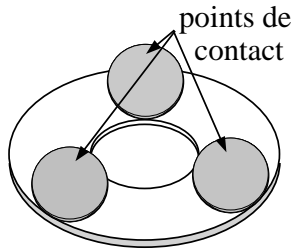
Partie mobile présentant trois points de contact en vue de dessus
